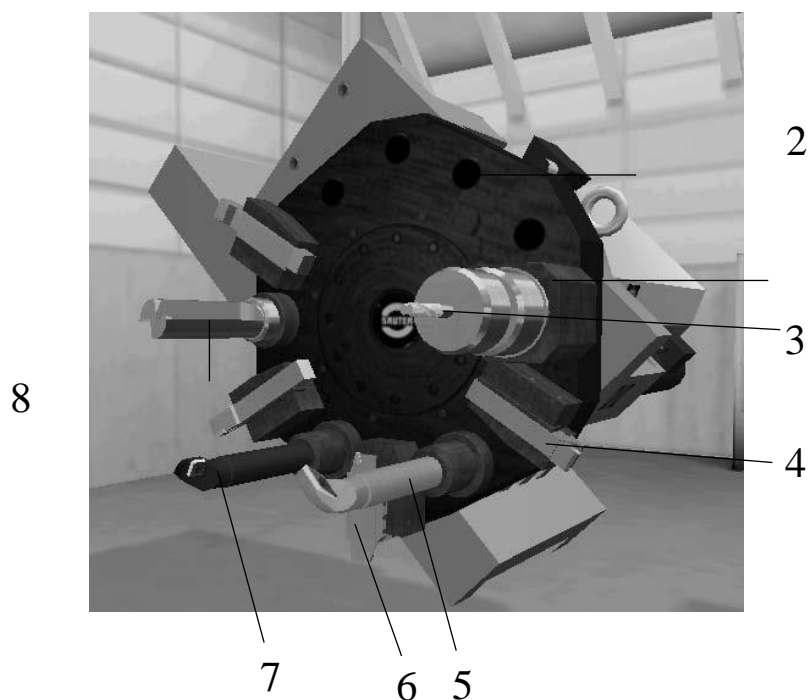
Общий вид револьверной головки токарного станка с ЧПУ
